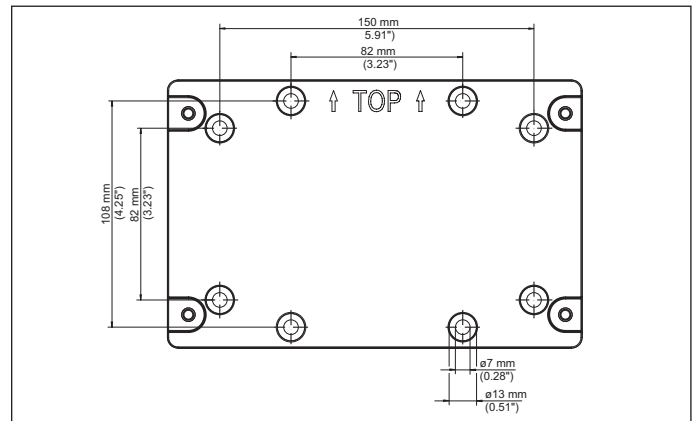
Montageplaat voor wandmontage (VEGAMET 861, 862)
